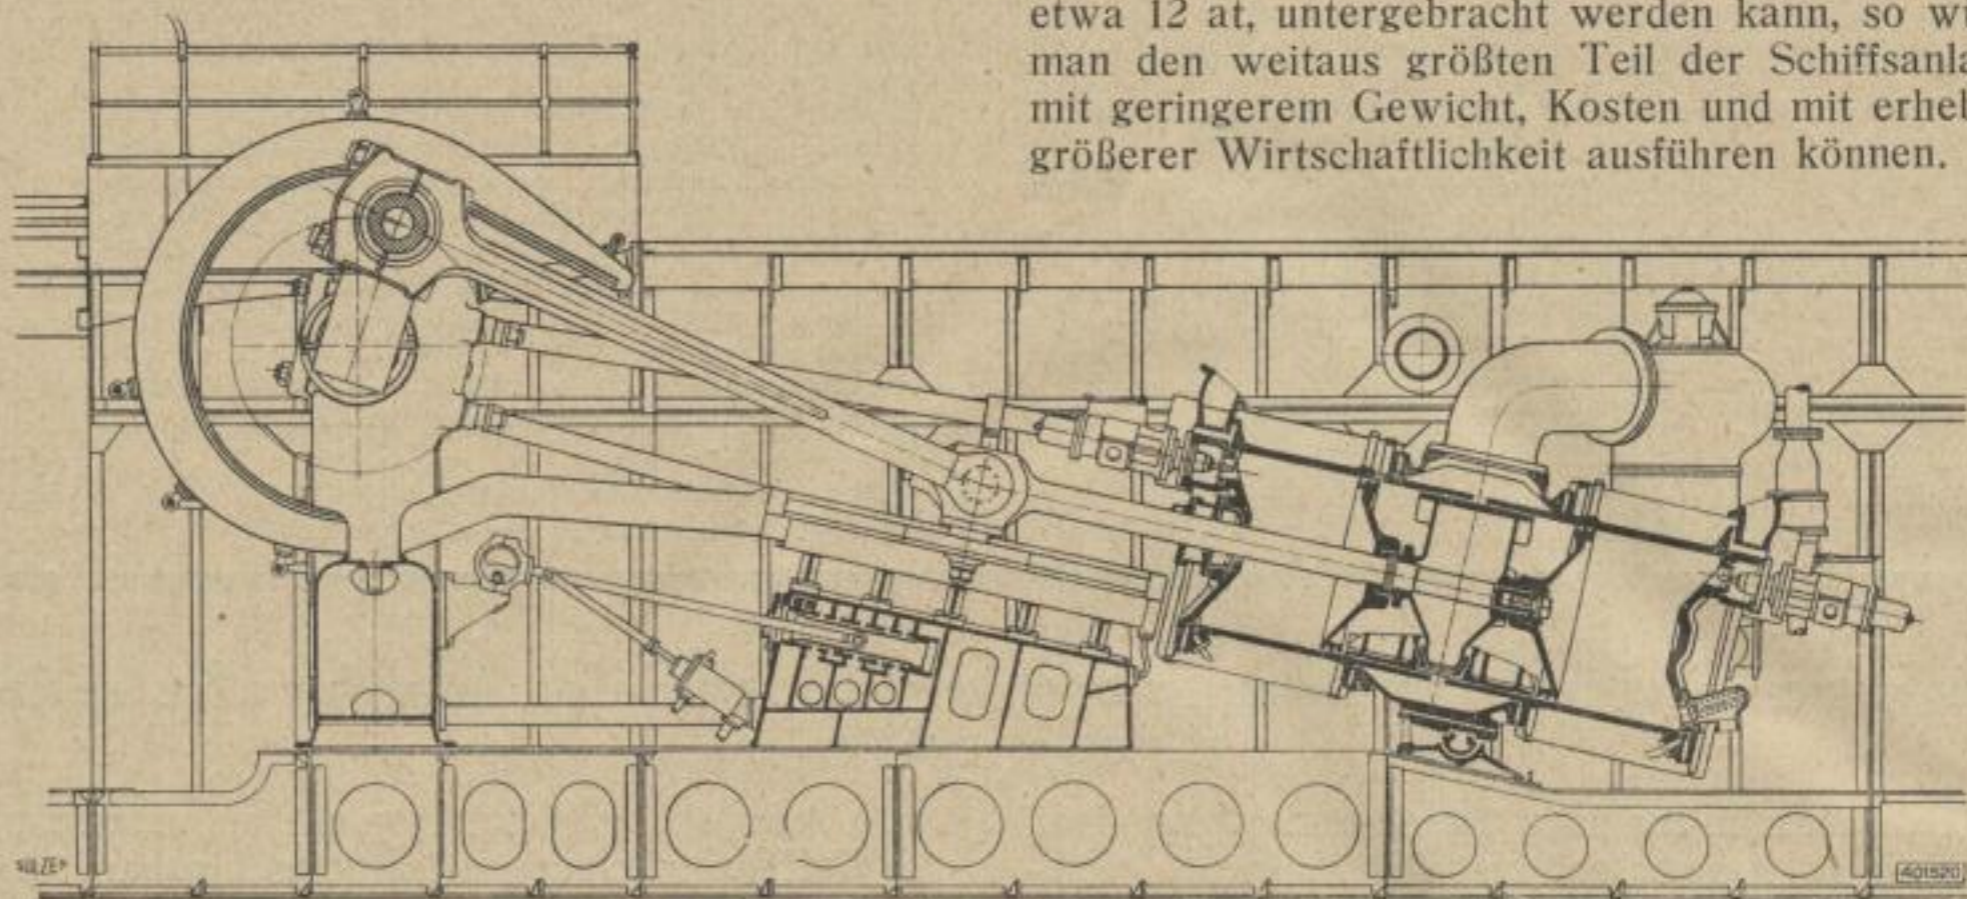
Seitenansicht der Gleichstromdampfmaschine.
